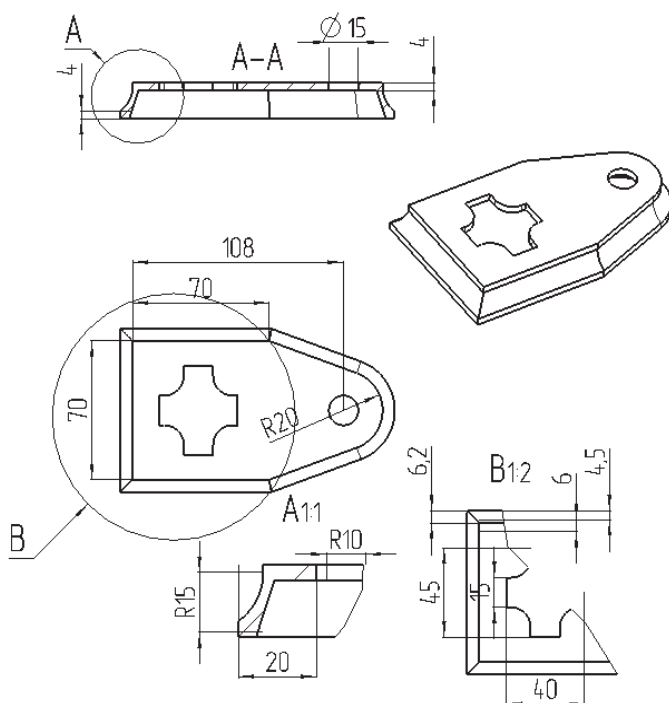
Габаритные размеры и общий вид литейной формы
